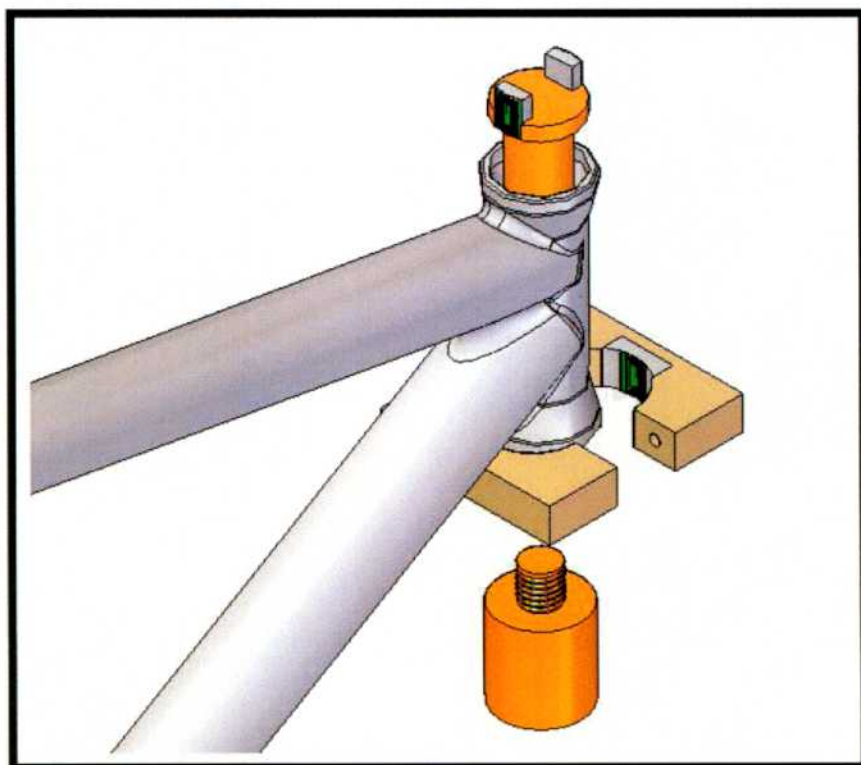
Dispositivo de medición montado en el tubo de dirección.
